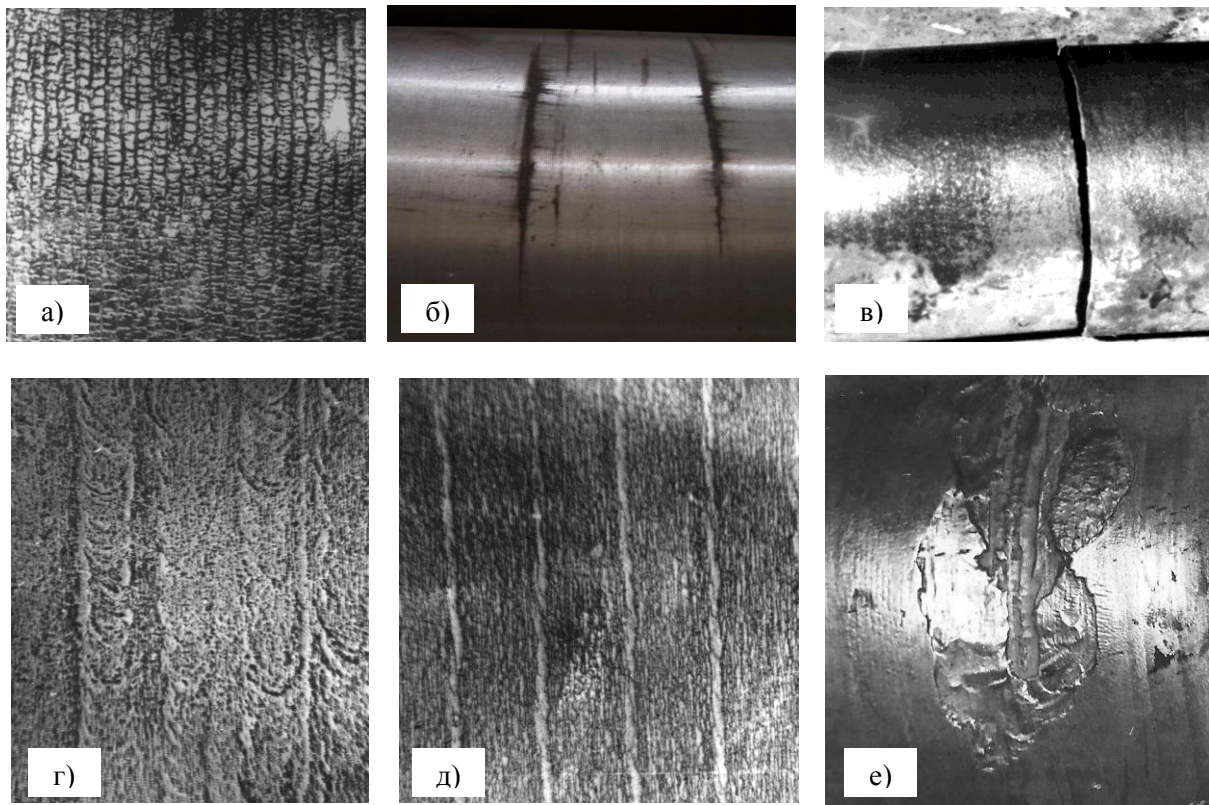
Износ и разрушение прокатного валка: а) трещины разгара на поверхности наплавленного металла; б) поверхность валка, восстановленная кольцевой наплавкой, с трещинами термической усталости; в) поломка валка по трещине термической усталости; г, д) кольцевой рельеф поверхности наплавленного металла, образованный при эксплуатации валка; е) откол рабочего слоя.
